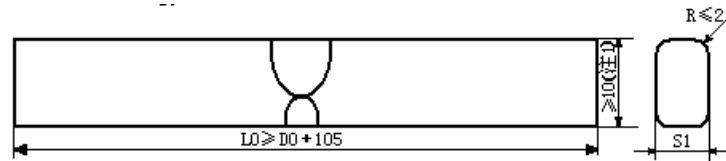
(b) 表 1 注 (3) 焊接位置弯曲试样的截取位置
